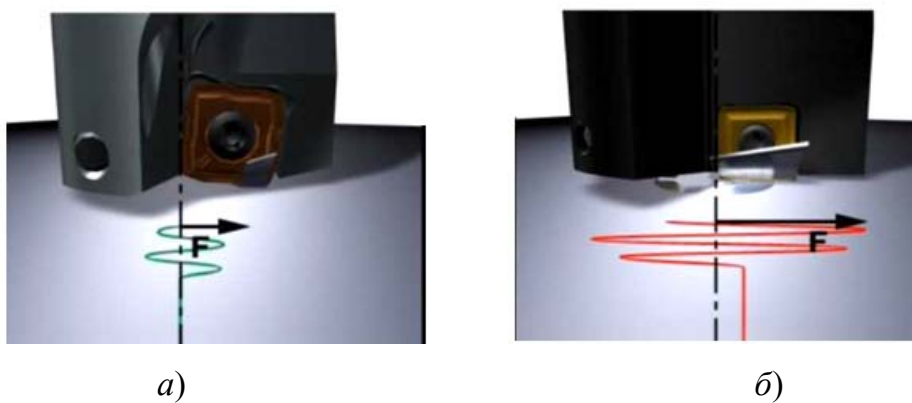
Схема процесса резания в обрабатываемый материал сборного сверла:
